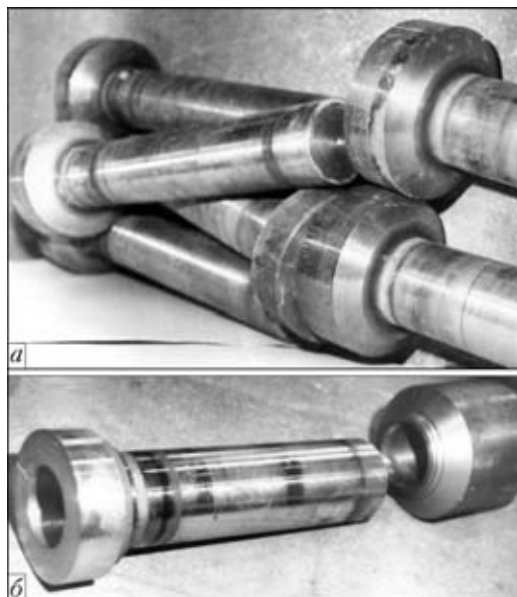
Сварные заготовки шлицевого (а) и шарнирного (б) валов
